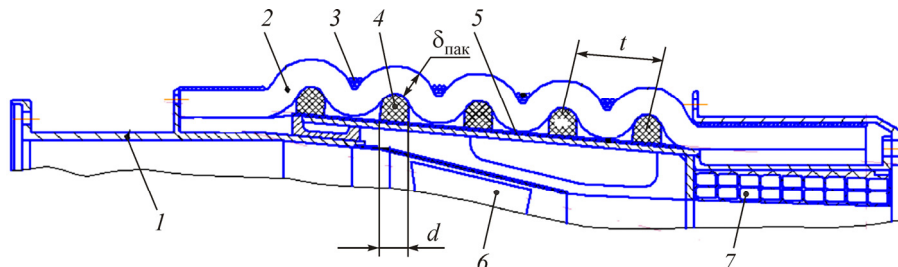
Конструкция гофрированного тканевого пакета, выполненная на металлическом корпусе: 1 – корпус; 2 – пакет ткани; 3 – кольцевые жгуты; 4 – резиновое кольцо; 5 – металлические лепестки; 6 – лопатка; 7 – панель шумоглушения
